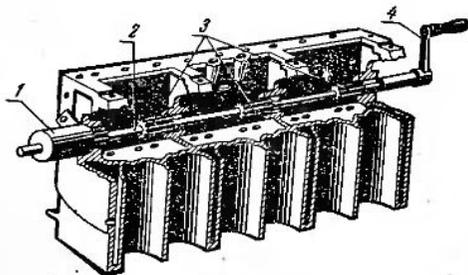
Развертывание втулок подшипников распределительного вала автомобильного двигателя:
